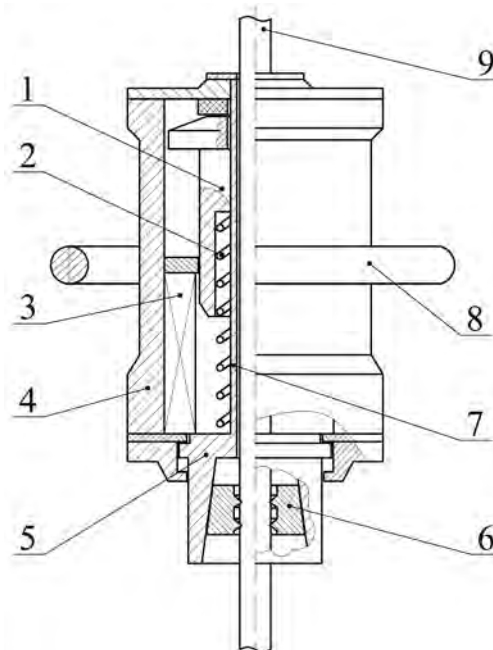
Ударник с ЛЭМД для неторцевого забивания продольно-неустойчивых стержней: 1 – якорь; 2 – пружина; 3 – обмотка; 4 – корпус-статор; 5 – наковальня; 6 – заклинивающие элементы; 7 – направляющая; 8 – рукоятка; 9 – стержень.
